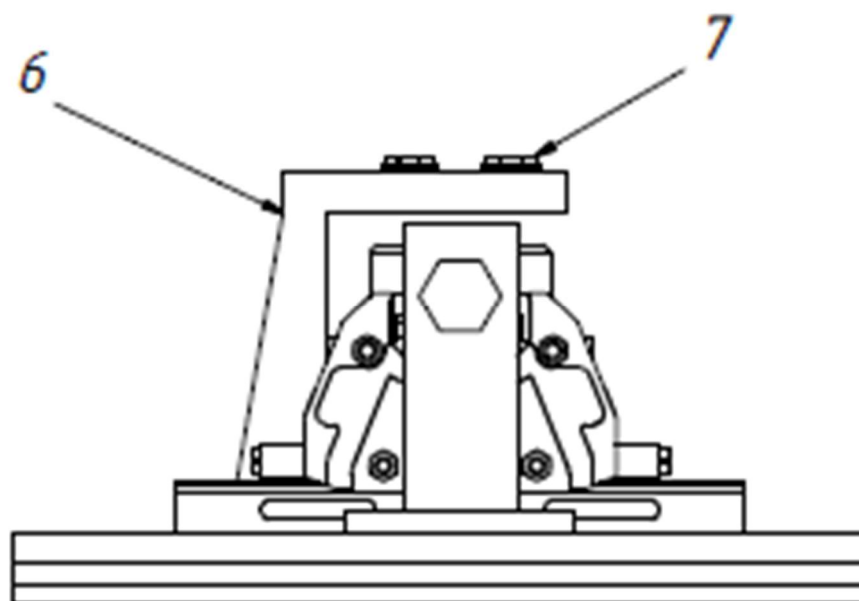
Свердильний пристрій (Вид 3)
